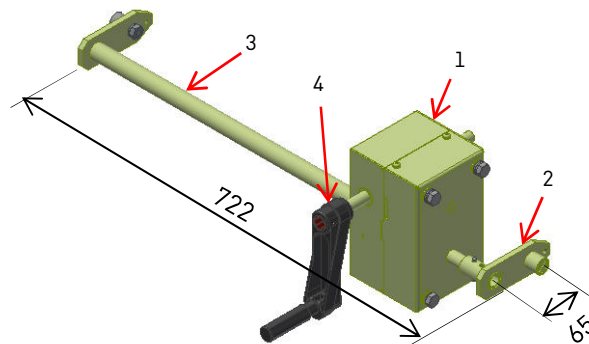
Схема узла блокировки и редукции ВЭ КРУ2-10.
